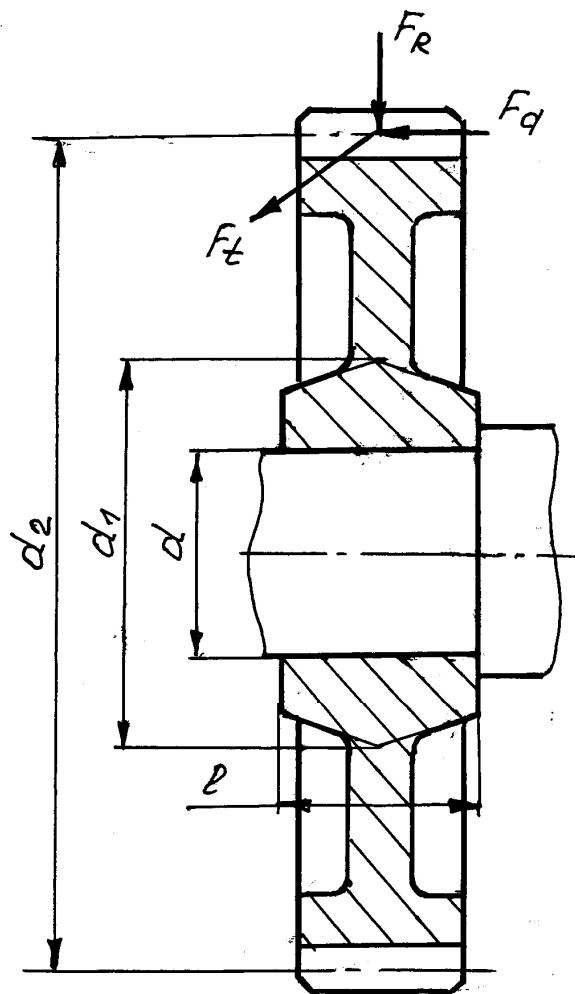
Передача момента соединением с натягом (расчет посадки по условию передачи требуемой нагрузки)
